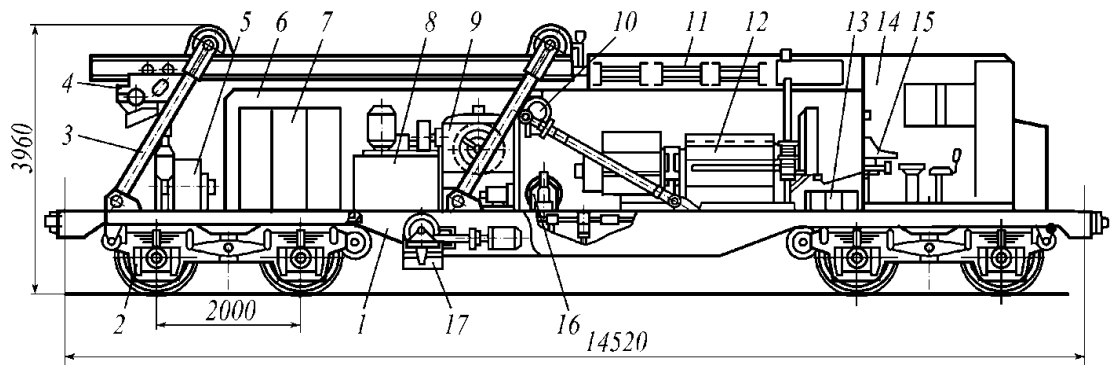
Схема рельсосварочной машины ПРСМ-4:
